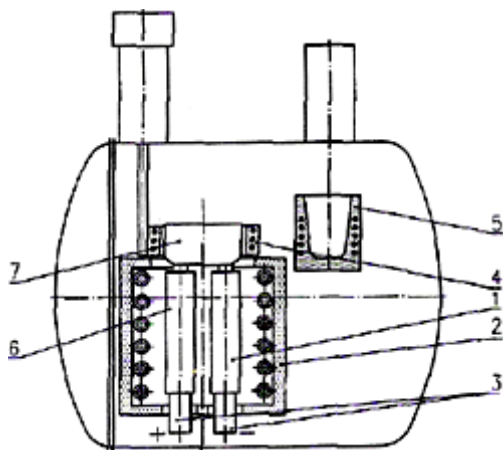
Схема плавильно-заливочной установки УПВ6-НК для отливки крупногабаритных лопаток турбины.
